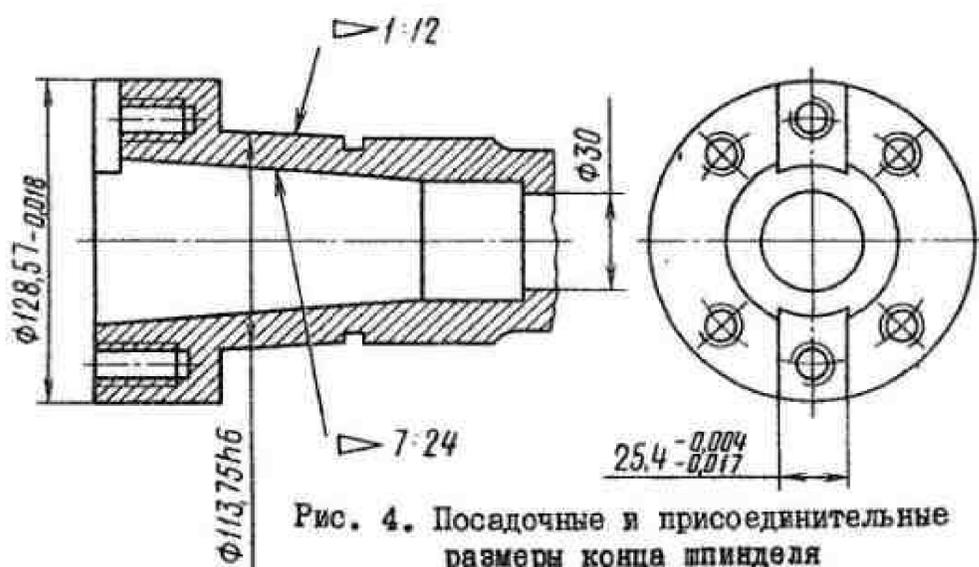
Посадочные и присоединительные размеры конца шпинделя
